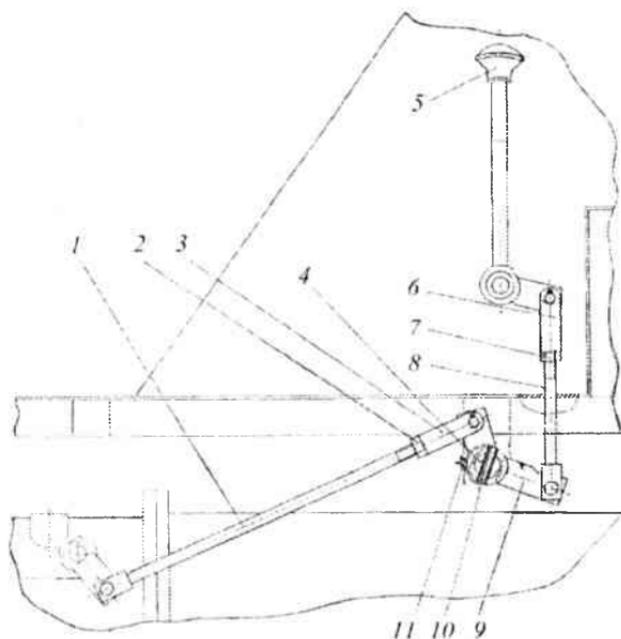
Управление приводом переднего ведущего моста: 1 – тяга; 2, 7 – гайка; 3 – вилка; 4 – вилка с рычагом; 5 – рукоятка рычага; 6 – рычаг управления; 8 – тяга; 9 – рычаг; 10 – штифт; 11 – проволока
